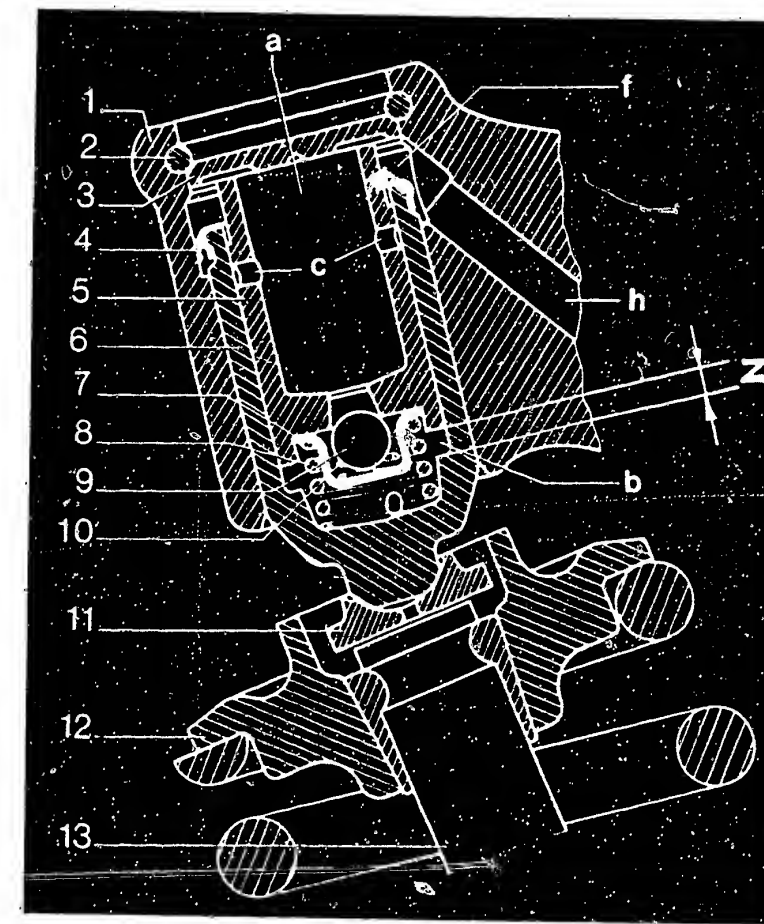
Hydraulisches Ventilspiel-Ausgleichselement der Benzinmotoren 102.924/962: 1 Kipphebel – 2 Sprengring – 3 Scheibe – 4 Verschlusskappe – 5 Druckbolzen – 6 Führungshülse – 7 Kugelführung – 8 Druckfeder – 9 Kugel d=4 mm – 10 Druckfeder – 11 Kugelpfanne – 12 Ventilfederteller – 13 Ventil – a Vorratsraum – b Arbeitsraum – c Rücklaufbohrung – f Ringkanal – h Ölkanal – z Kontrollmass.
